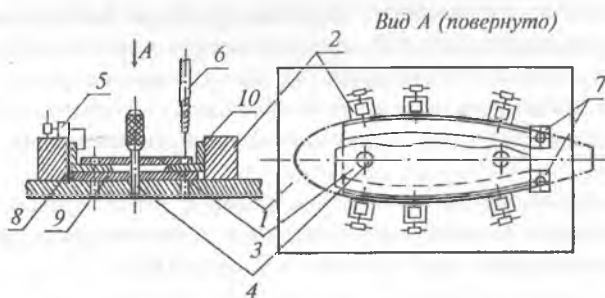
Схема сборки нервюры в сборочном приспособлении: 1 — плита; 2 — опорный элемент приспособления (ложемент); 3 — кондуктор; 4 — штифт; 5 — прижим; 6 — сверло; 7 — упоры; 8 и 10 — пояса нервюры; 9 — стенка нервюры
